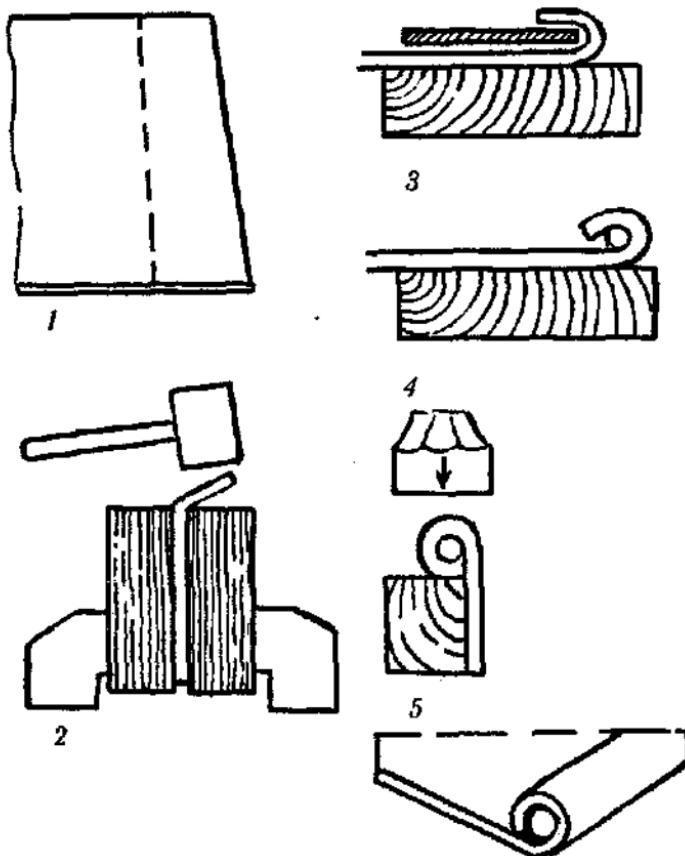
Изготовление края с усилением. Дополнительную жесткость край листа приобретает, если положить под загиб проволоку и закатать ее: 1 — край листа размечают: ширина загибающей части равна двум диаметрам проволоки плюс двойная толщина листа; 2 — край отгибают под углом в 90°; 3 — край загибают по прокладке из металла; 4 — кромку листа окончательно загибают на деревянной оправке,
